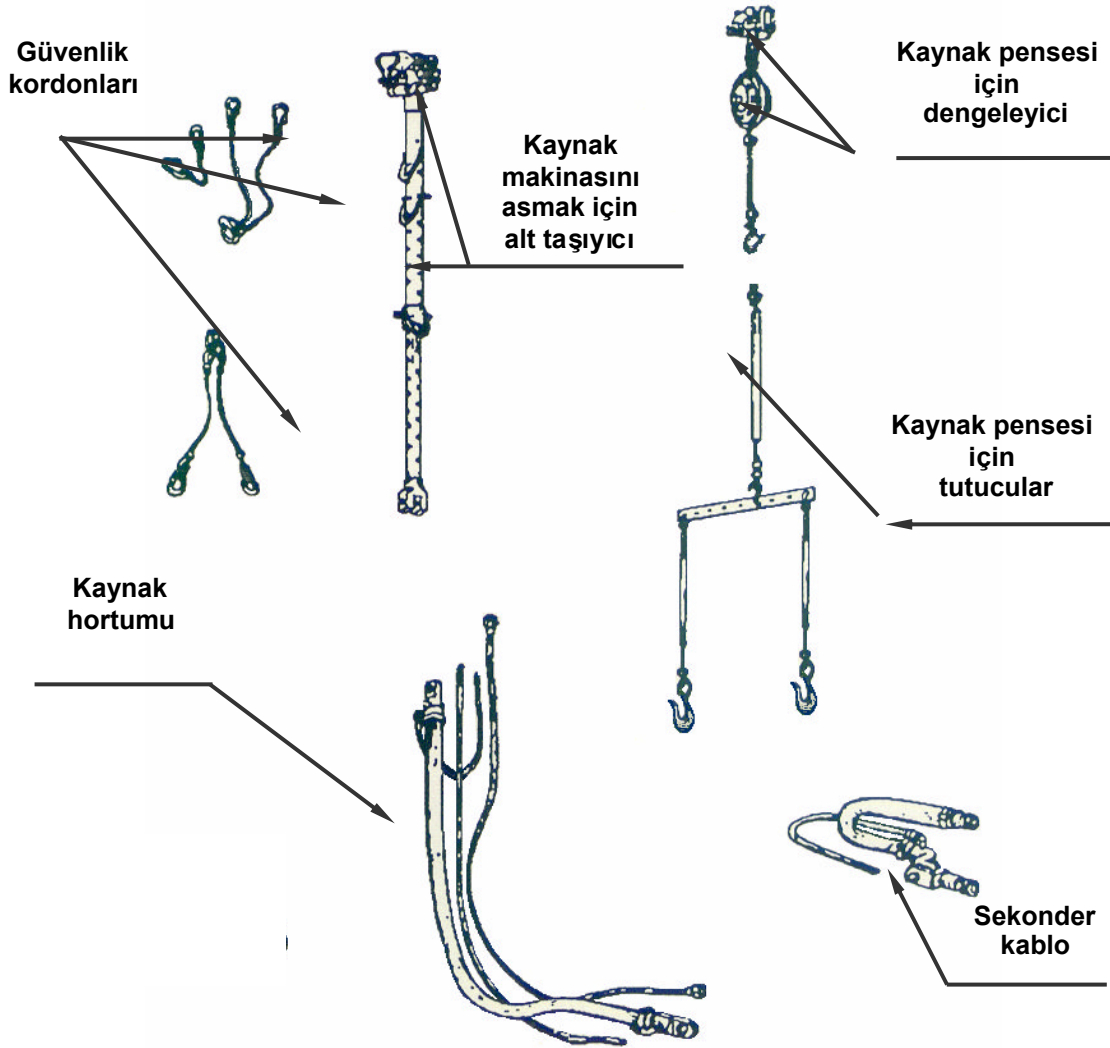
Askılı Kaynak Makinasının Parçaları
